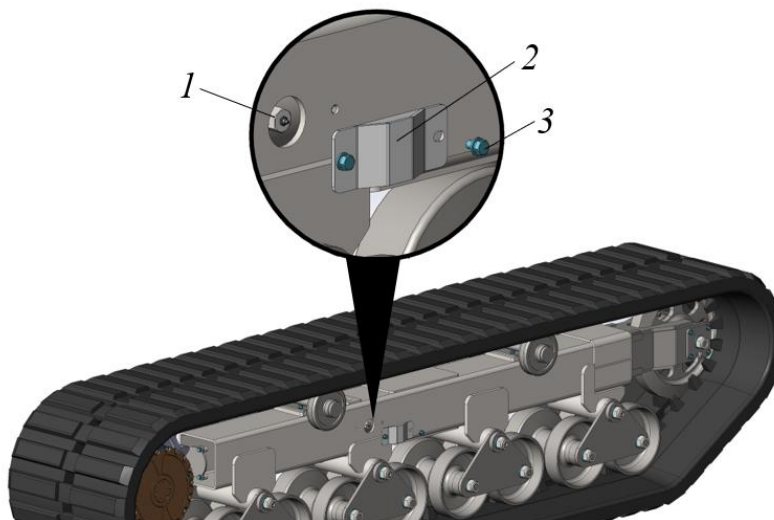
Месторасположение пресс-масленки механизма натяжения гусениц
